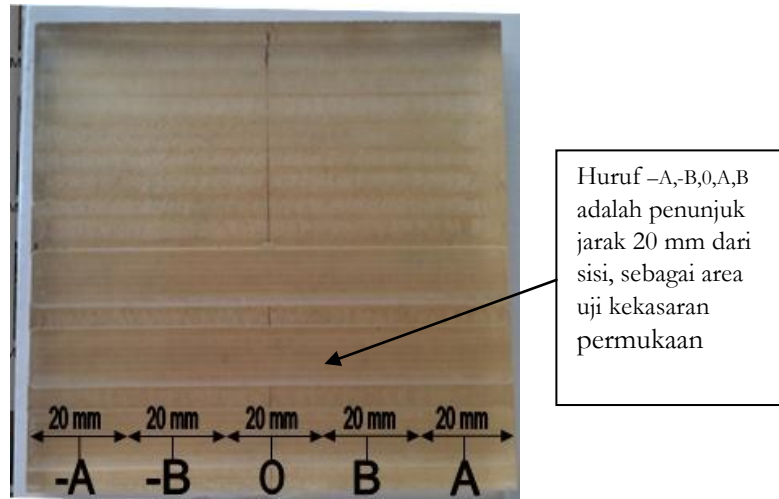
Foto makro spesimen 8 (Kecepatan *spindle* 7500 Rpm, *Feed rate* 400 mm/min dan *Tool path Parallel Spiral*)
